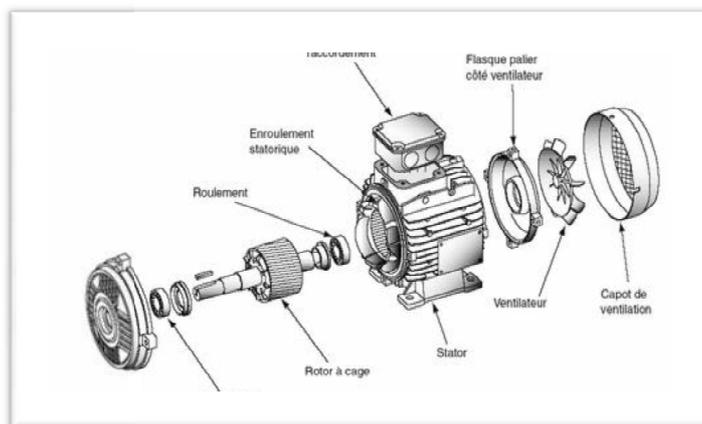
Vue générale d'une coupe d'un moteur asynchrone
